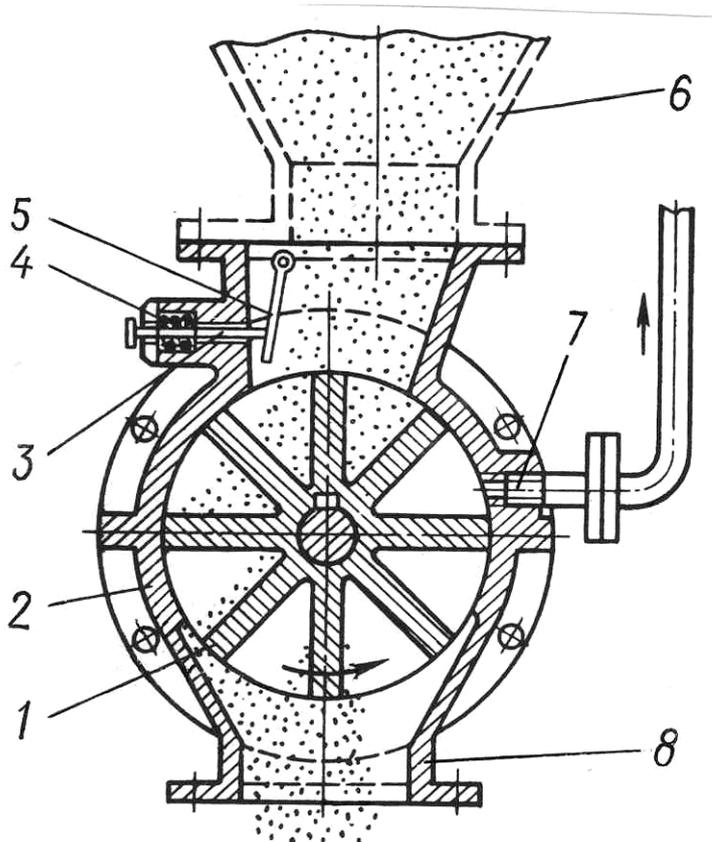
Шлюзовой затвор: 1 – лопастной барабан; 2 – корпус; 3 – штифт; 4 – пружина; 5 – скребок; 6 – приемный патрубок; 7 – труба для выравнивания давления в ячейке барабана и аппарата; 8 – разгрузочный патрубок
